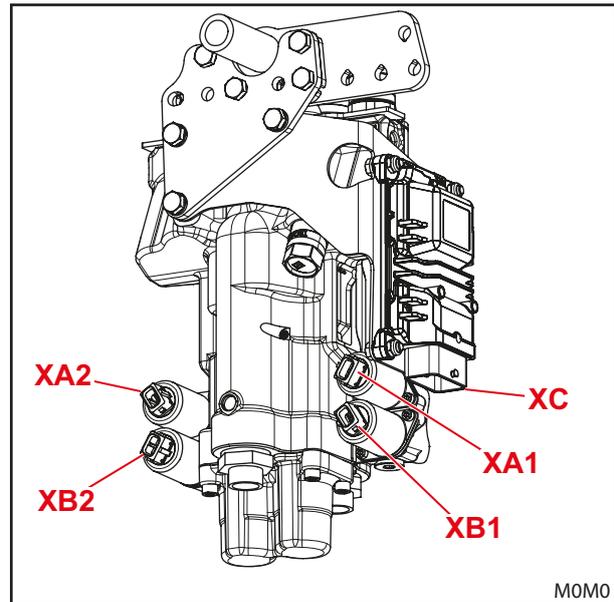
Pro Control – Übersicht über die Stecker am Hydac-Ventil
